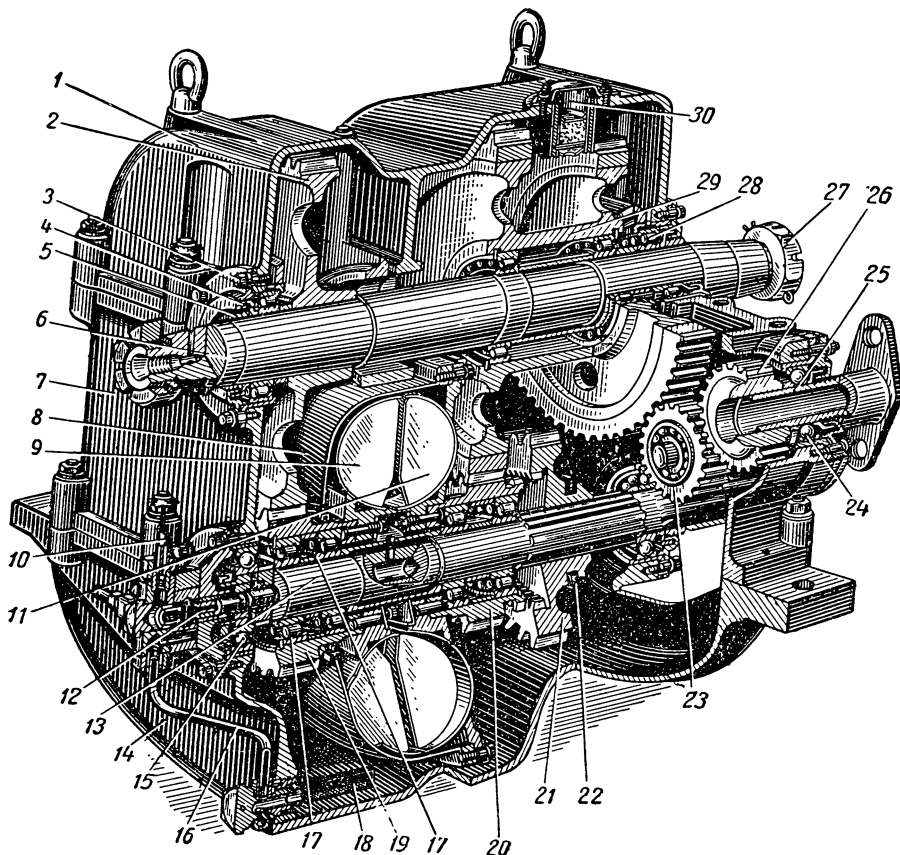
Общий вид гидромеханического редуктора с приводом компрессора непосредственно от коленчатого вала дизеля:
